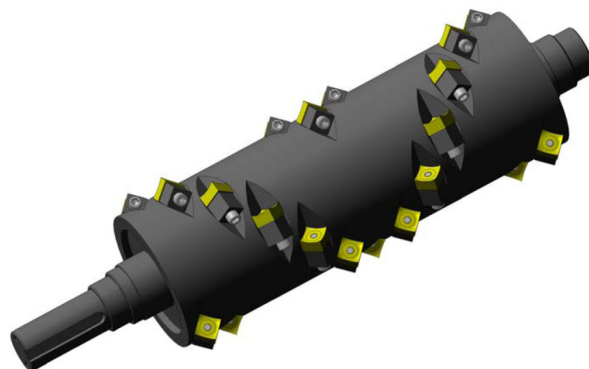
3D-модель сборочной единицы «Ротор» из сборки «Корпус шредера»
